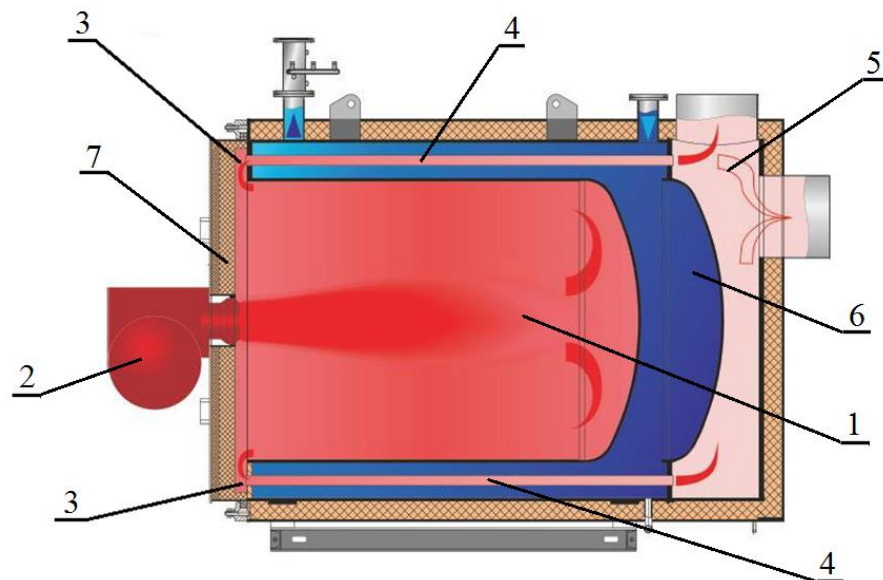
Конструктивная схема газового тракта котла ТТ-500 [108]: 1 – жаровая труба; 2 – горелка; 3 – поворотная камера; 4 – конвективный пучок дымогарных труб; 5 – сборный дымовой короб; 6 – водяной объем; 7 – крышка.
